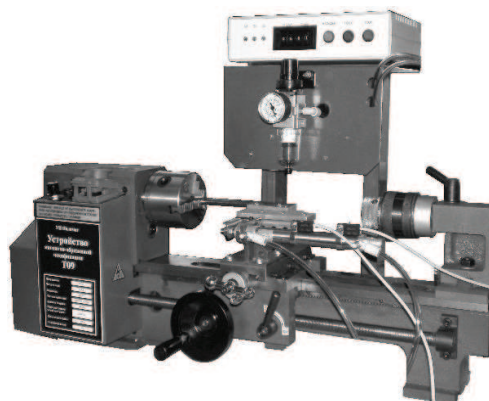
Общий вид установки Т09 для магнитно-абразивной обработки труб.
